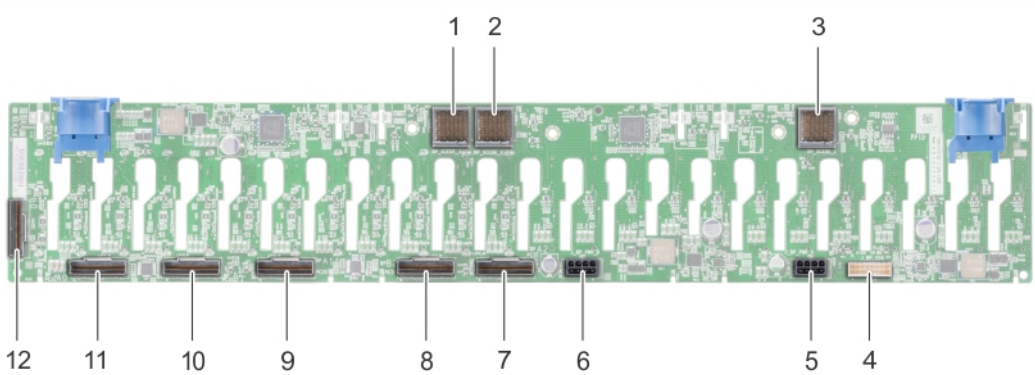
Vue arrière du fond de panier de 24 disques de 2,5 pouces
